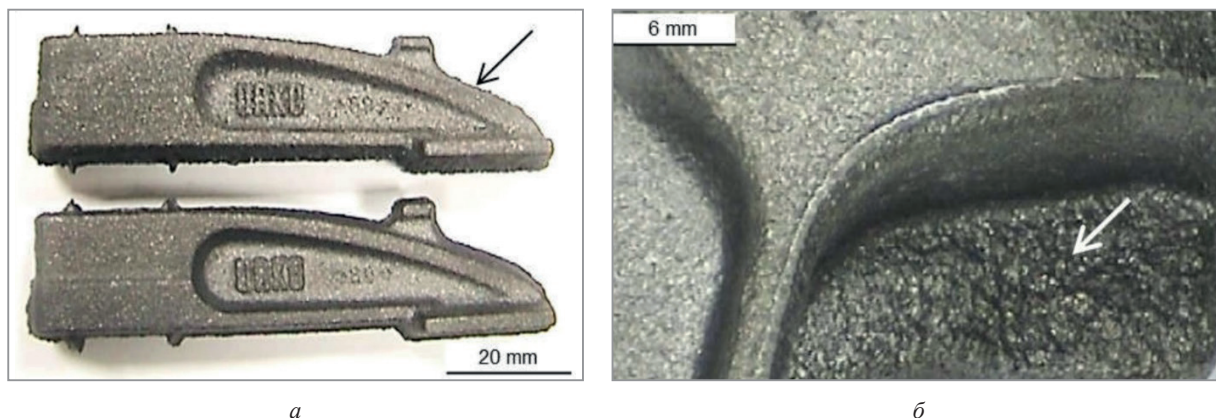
Дефекты отливки «Грубая шероховатость»
